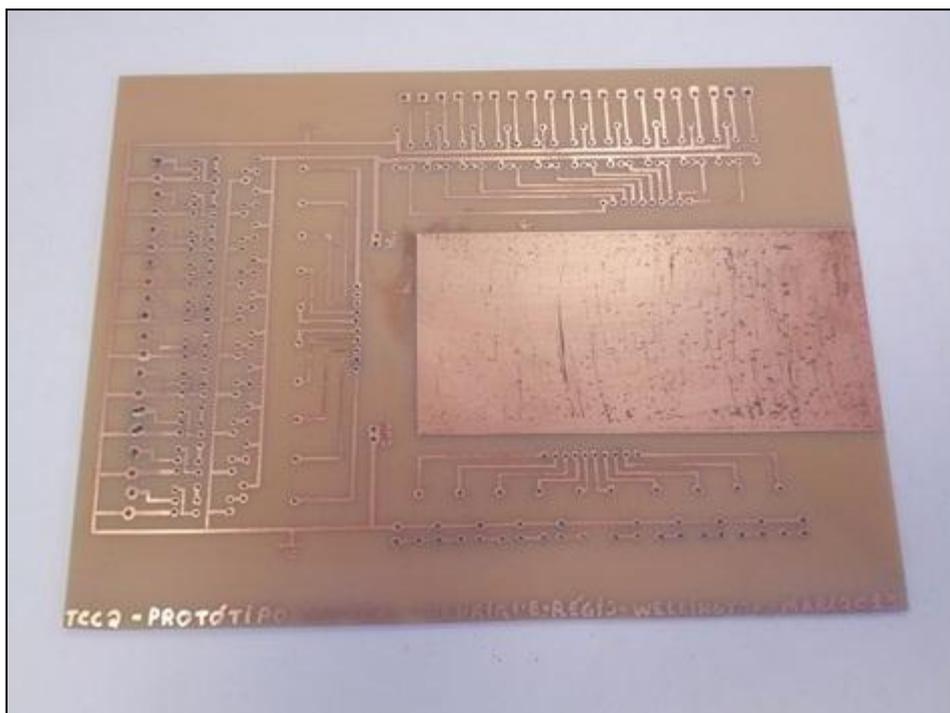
Placa de circuito impresso corroída para montagem final do projeto
